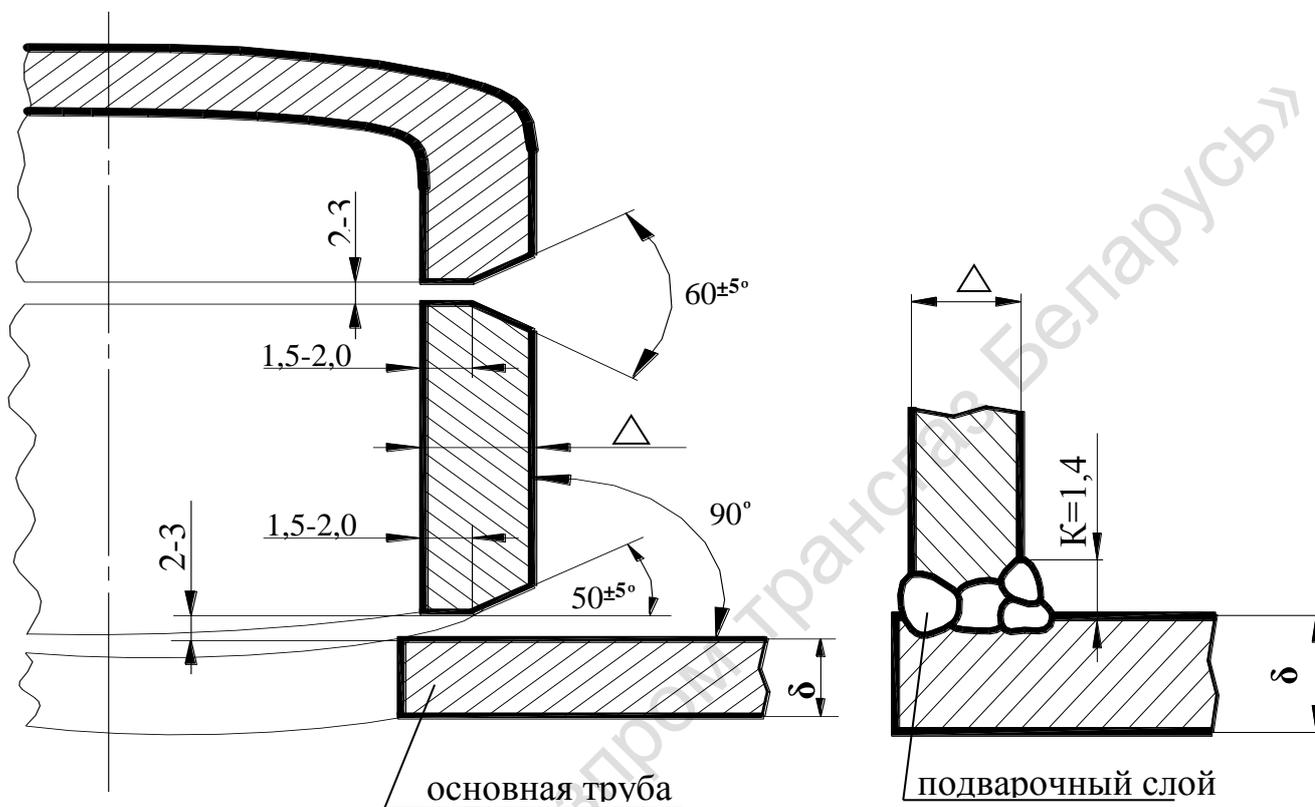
Схема подготовки под сварку при заварке технологических отверстий с помощью патрубков
